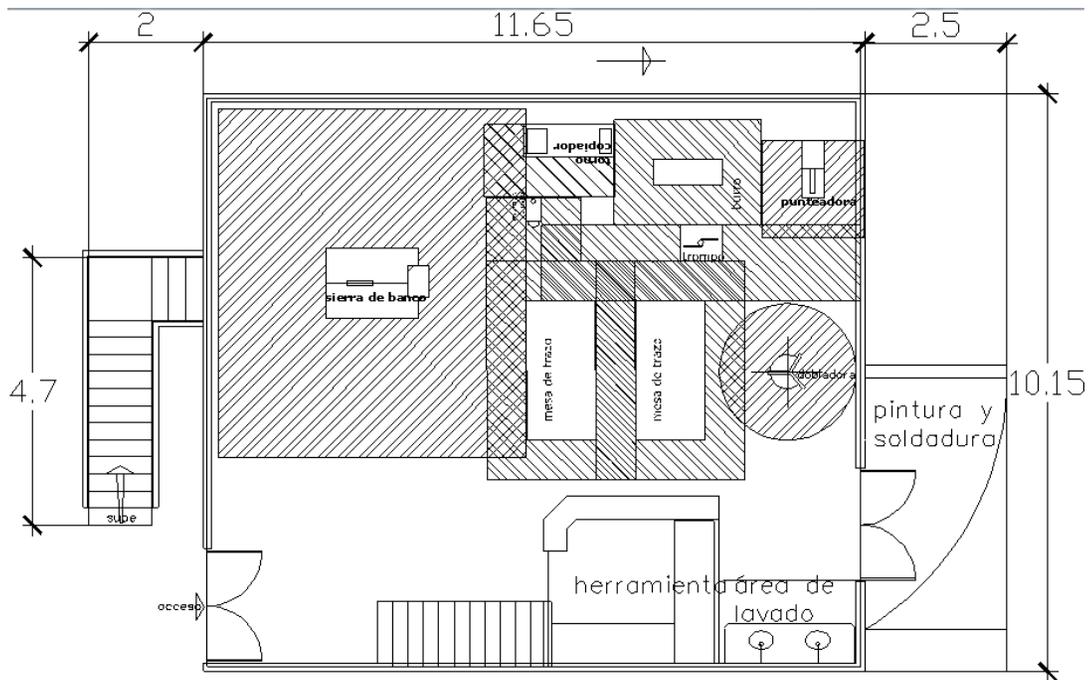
Distribución de la planta baja con áreas de trabajo (taller carpintería-herrería).
